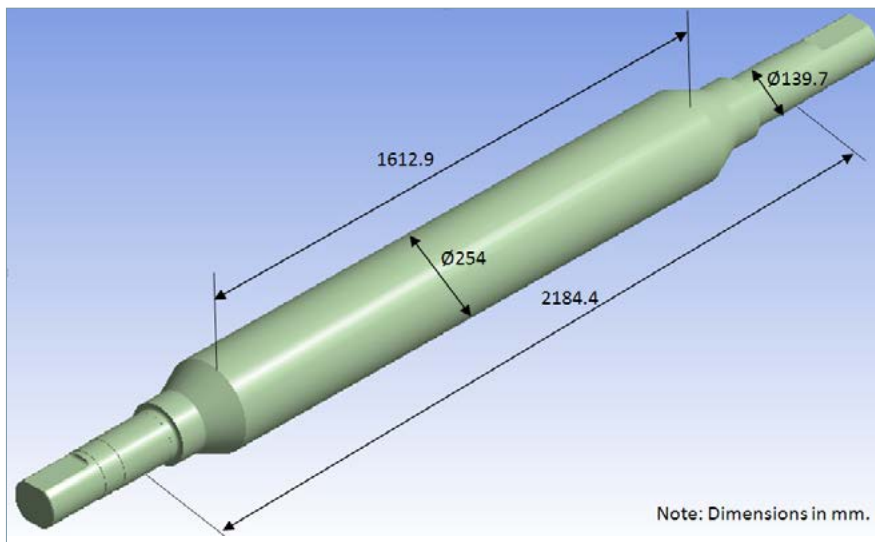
Diseño de rodillo de trabajo; vista isométrica
